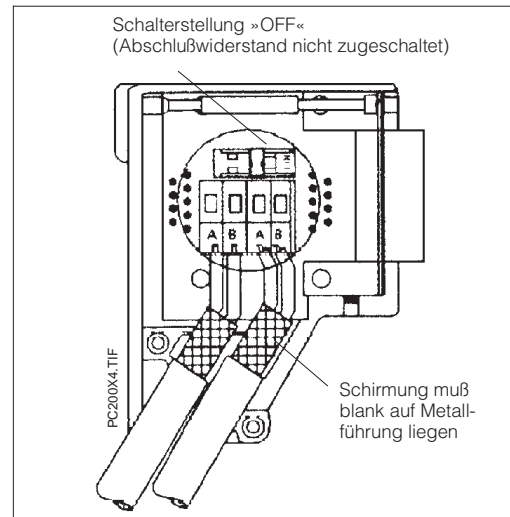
Busanschlußstecker geöffnet (rechts)
